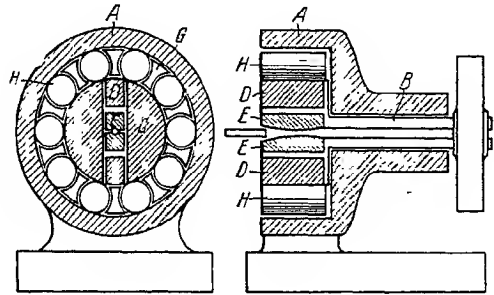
Hämmertaschine für Wolframstäbe. A Gehäuse; B Achse zum Hämmerkopf; C Hämmerkopf; D Schlagbacken; E Hämmerbacken; G Rollenkäfig; H Rollen.
